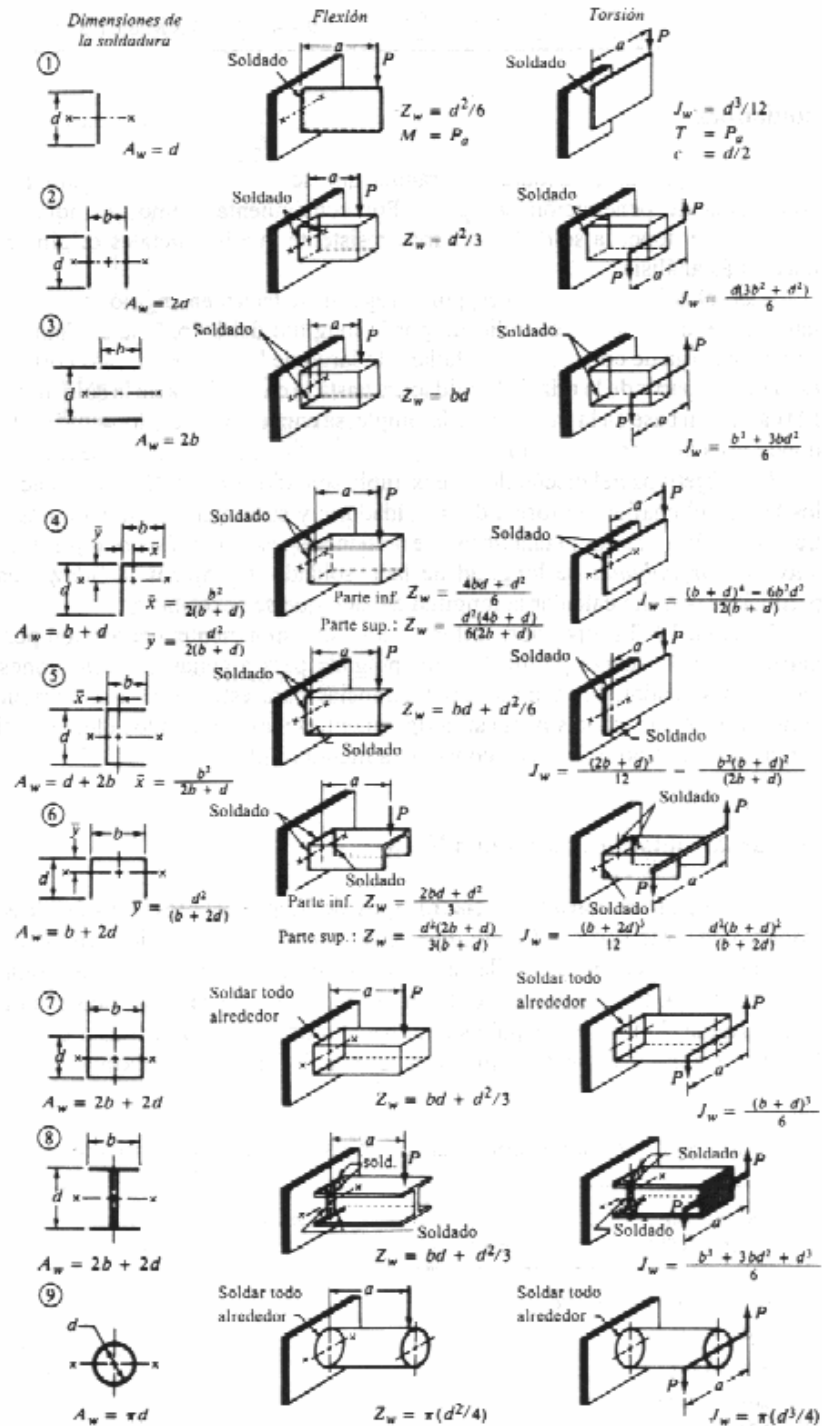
Factores de geometría para análisis de soldadura.
